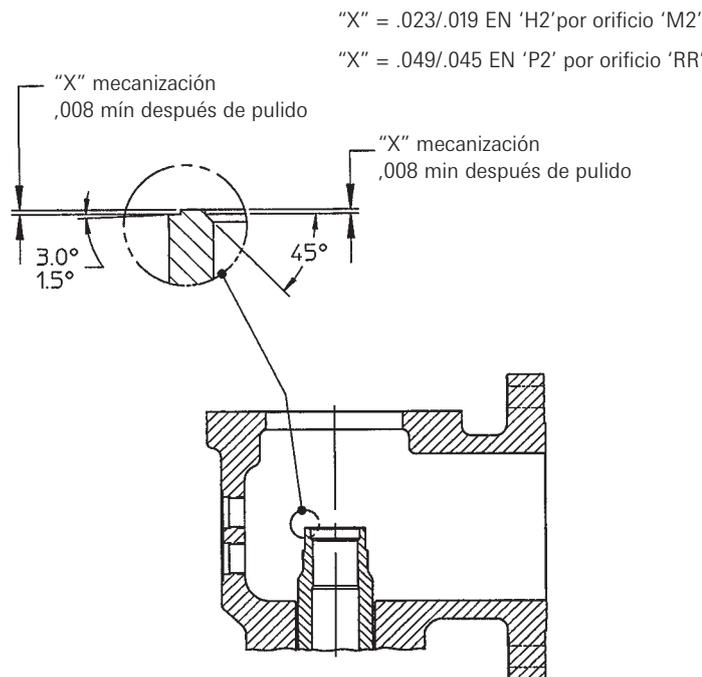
Dimensiones Críticas de Asiento de Boquilla
